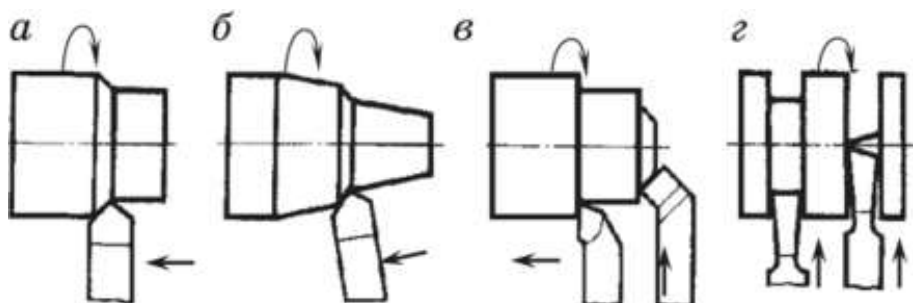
Схеми обробки зовнішніх циліндричних поверхонь на токарних верстатах.
